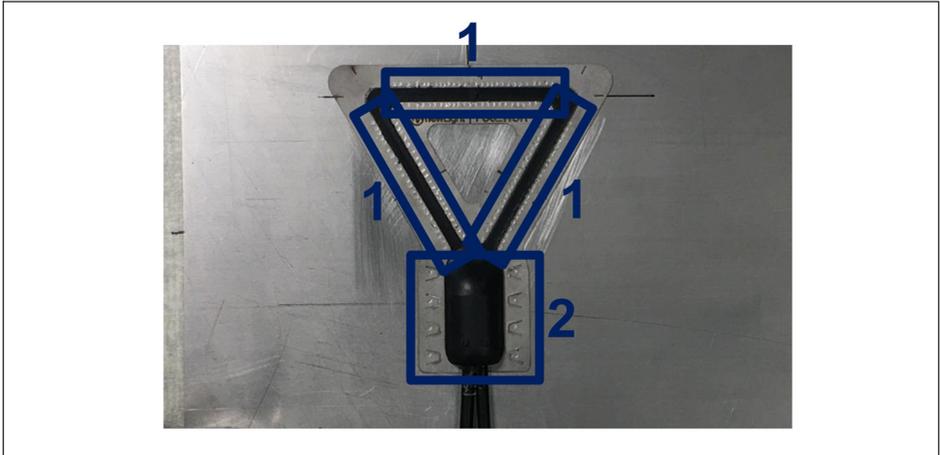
Schweißflächen des FS62WSR
